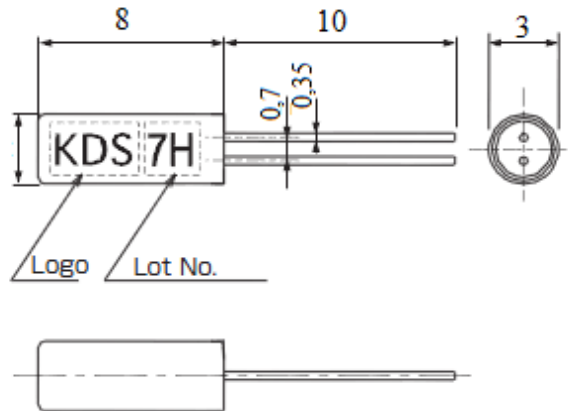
Габаритні розміри кварцового резонатора DT-38
